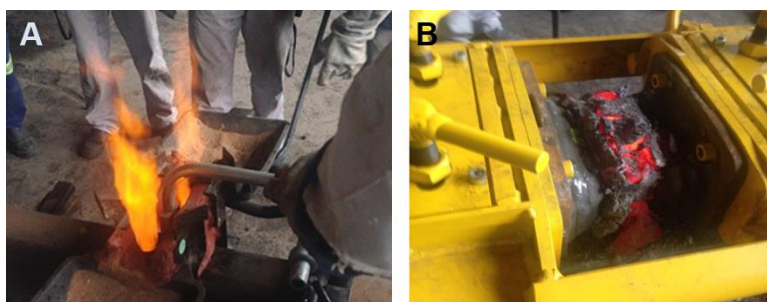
Pré aquecimento e rebarbagem no processo de soldagem TW
